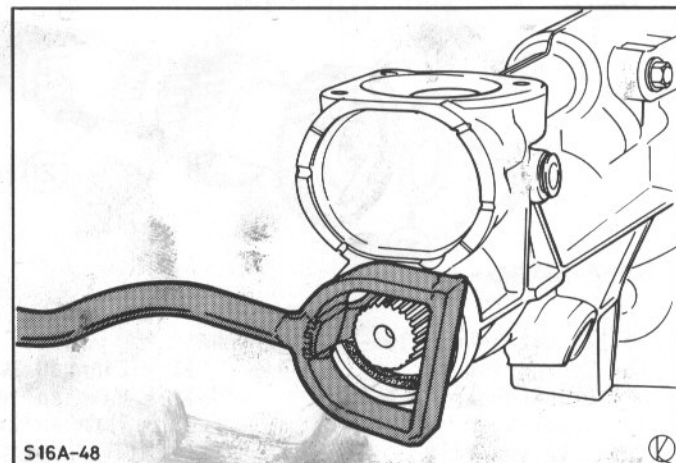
Radialdichtring mit Spezialwerkzeug ausbauen
